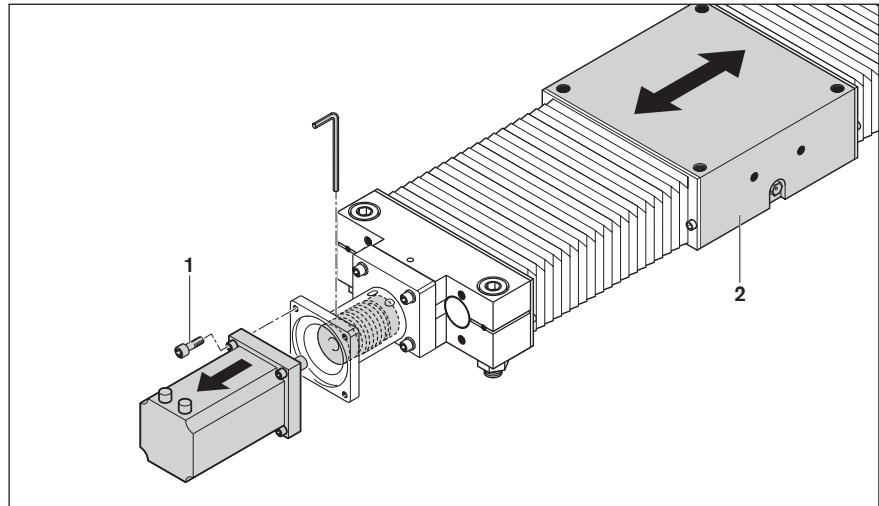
Motor demontieren / Flansch und Balgkupplung
